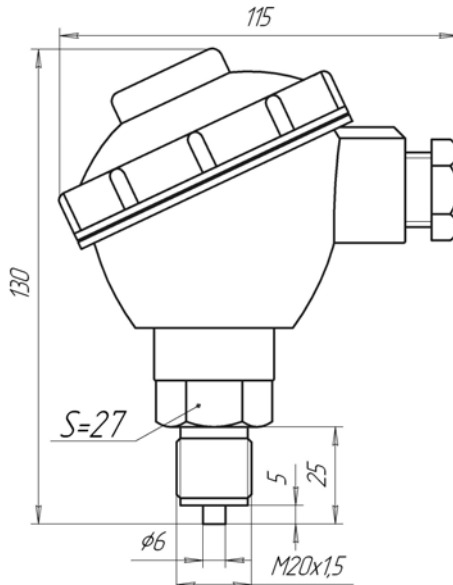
Модель 1015. Литой корпус. Гермоввод кабеля.
